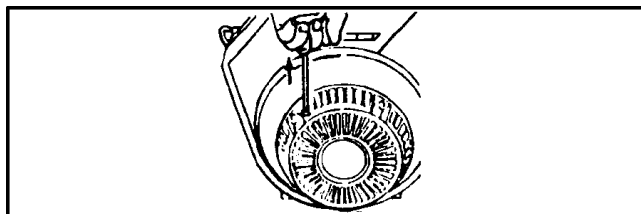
Démarreur enrouleur - Moteur Vanguard.
